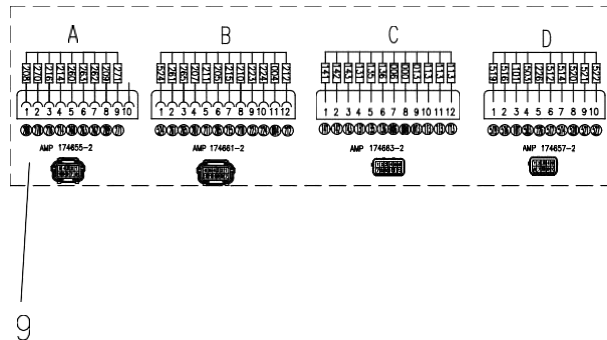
Montaje del dispositivo de control E30T-E35T
